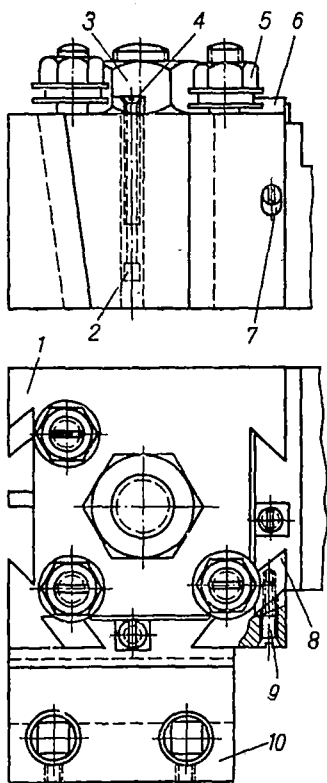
Резцовая головка с несколькими взаимозаменяемыми резцедержателями.
